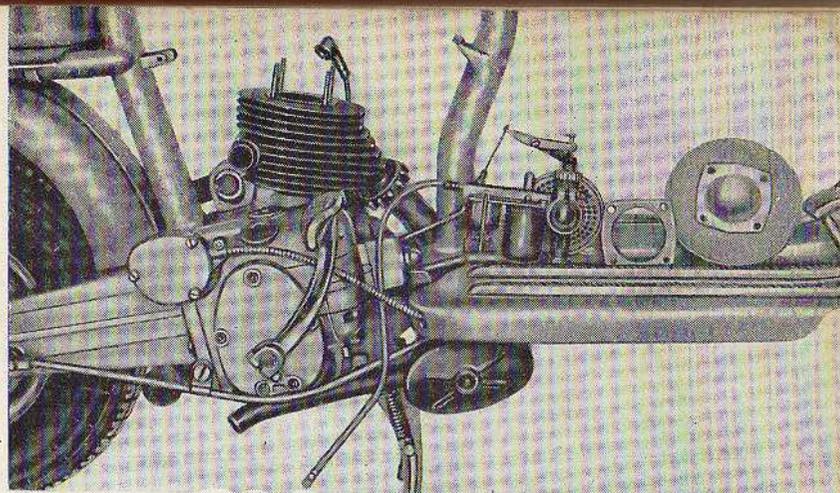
Desmontaje carburador y cabeza del cilindro
